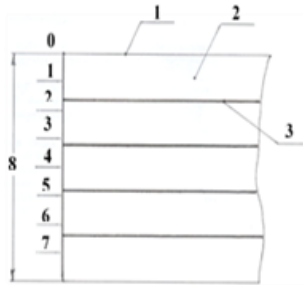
Схема пакета печатных плат из 5 пластин.
